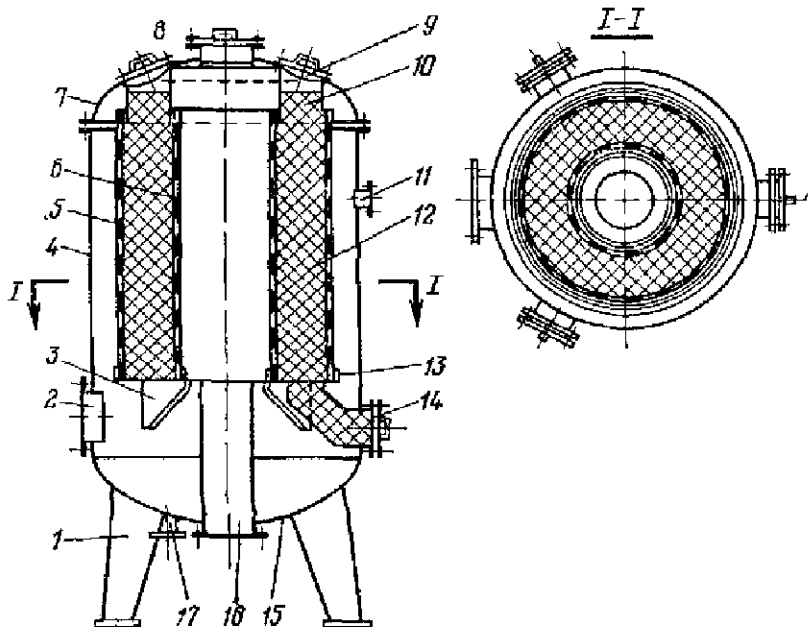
Кольцевой адсорбер: 1 – установочная лапа; 2 – штуцер для подачи паровоздушной смеси, сушильного и охлаждающего воздуха; 3 – опора для базы под цилиндры; 4 – корпус; 5, 6 – внешний и внутренний перфорированные цилиндры; 7 – крышка; 8 – смотровой люк; 9 – загрузочный люк; 10 – бункер-компенсатор; 11 – штуцер для предохранительного клапана; 12 – слой активного угля; 13 – база для цилиндров; 14 – разгрузочный люк; 15 – днище; 16 – штуцер для отвода очищенного и отработанного воздуха и для подачи водяного пара; 17 – штуцер для отвода паров и конденсата при десорбции и для подачи воды
